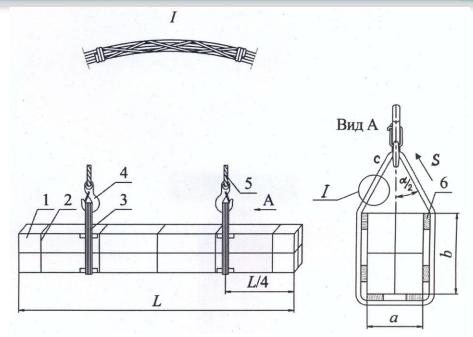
Общий вид специального грузозахватного проволочного приспособления: 1— длинномерный груз в виде четырех заготовок; 2 — металлические скрутки пакета заготовок; 3 — ГПП; 4 — чалочный крюк траверсы; 5 — строп траверсы; 6 — деревянная подкладка
